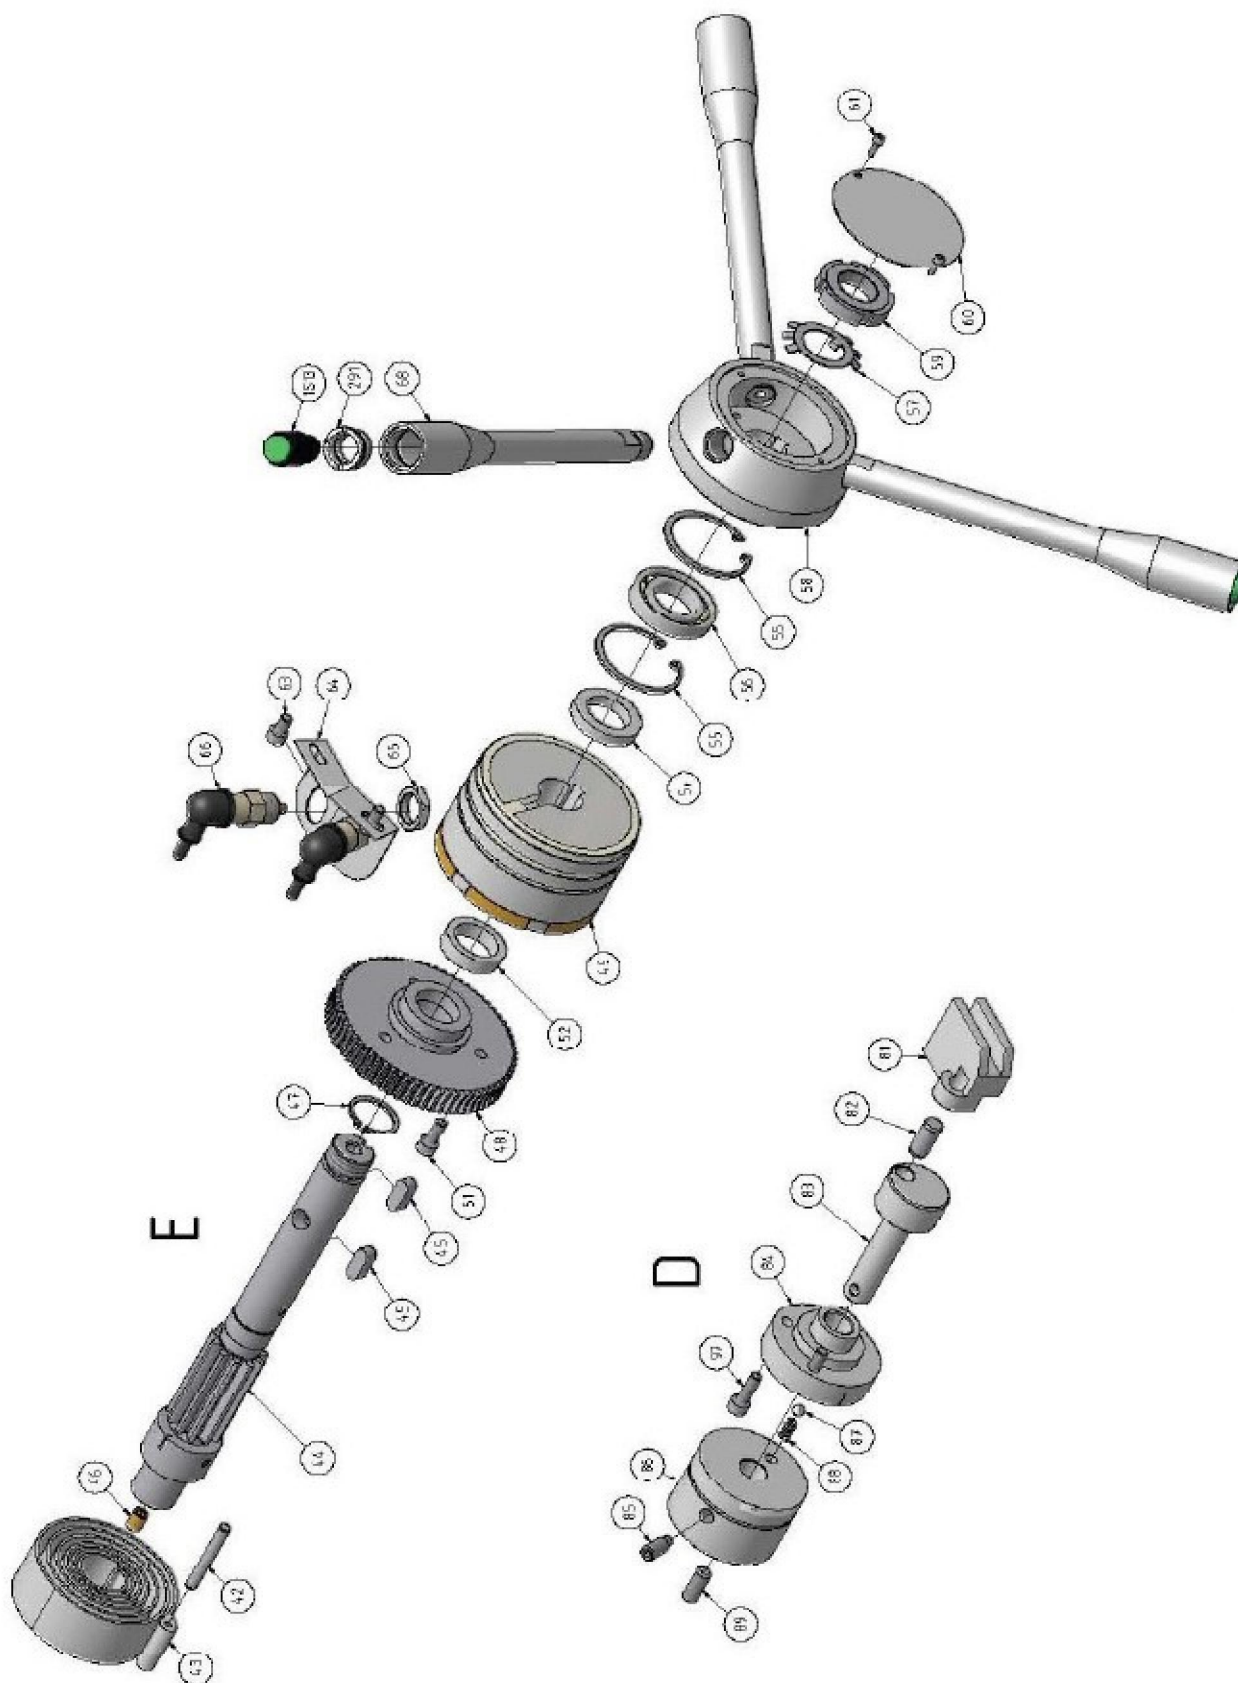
Caja de engranajes de avance 2 de 4 - Feed gear box 2 of 4
